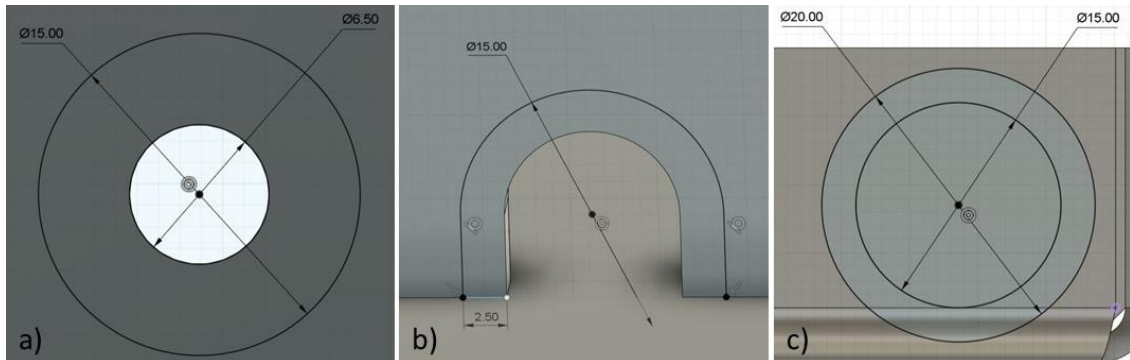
Zonas preservadas: a) furos fixação; b) "slots" de amarração; c) passagem cablagem principal
